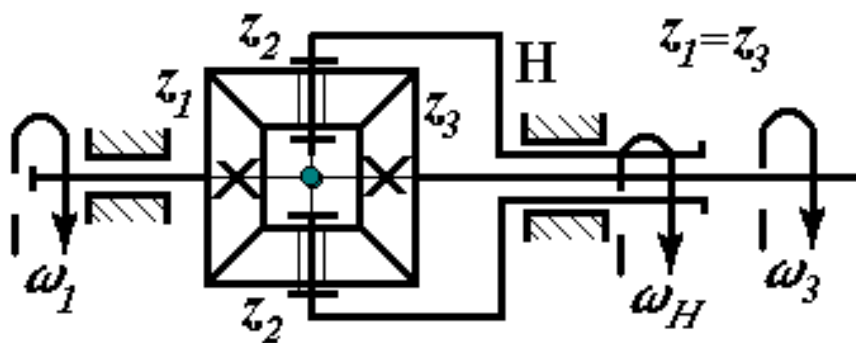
Кинематическая схема дифференциала с коническими зубчатыми колесами
